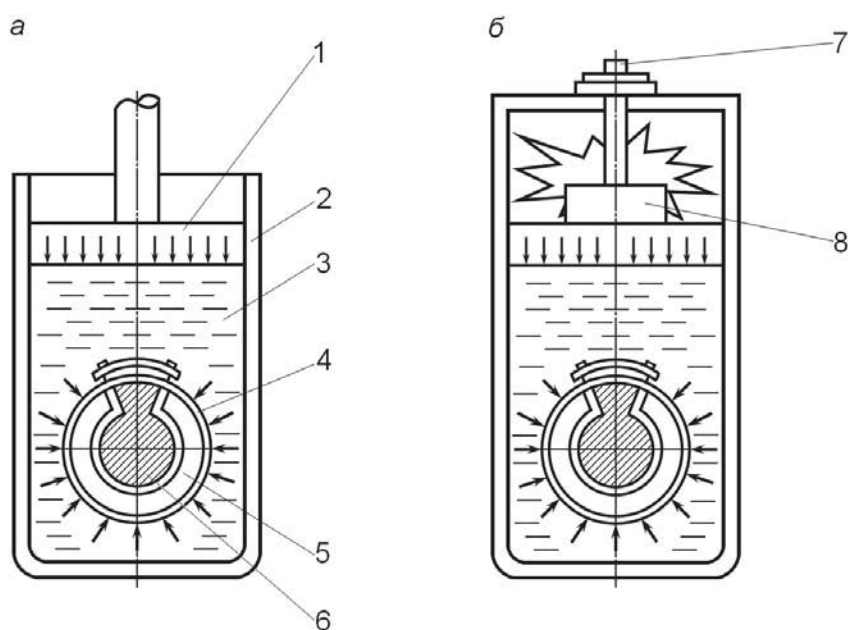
Схеми гідростатичного (*а*) та вибухового (*б*) пресування: 1 – пуансон; 2 – прес-камера; 3 – робоча рідина; 4 – гумова оболонка; 5 – деталь, що формуються; 6 – сталеве осердя; 7 – запал; 8 – заряд вибухової речовини
